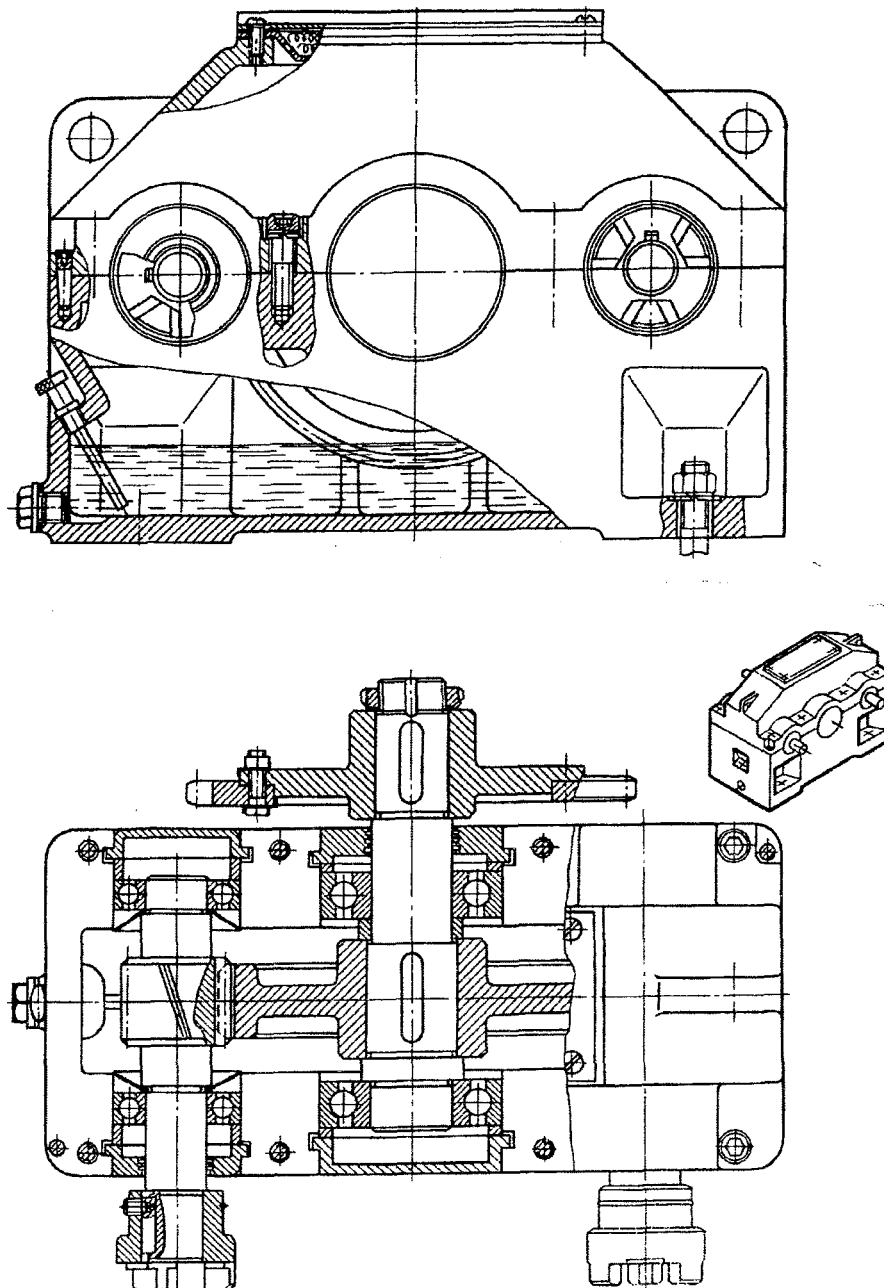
Цилиндрический горизонтальный одноступенчатый редуктор с двумя быстроходными валами [4]
